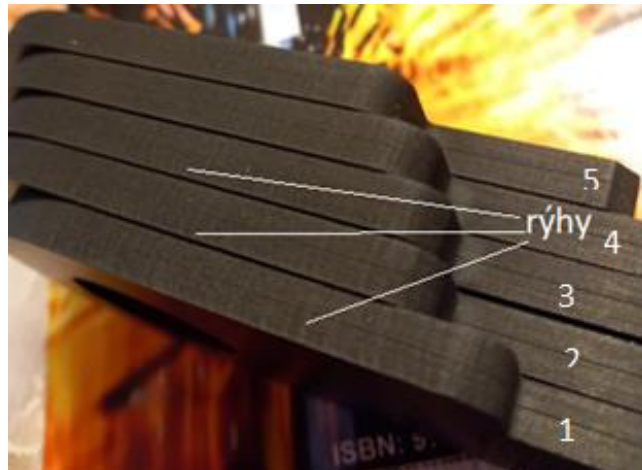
Reliéf obrobeneho povrchu AWJ [62].
